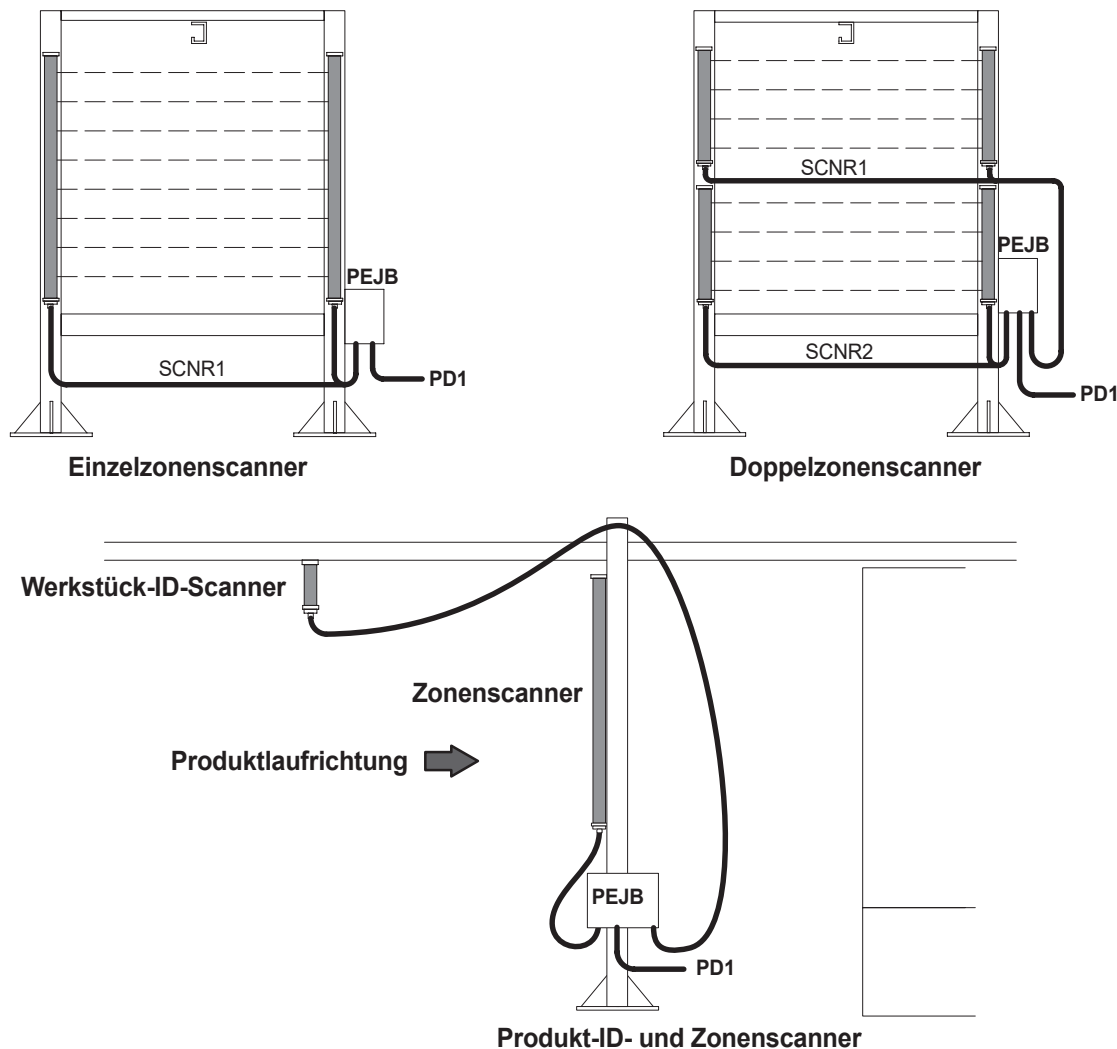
Kabelanschlüsse für Zonen- und Werkstück-ID-Scanner (typisch)
